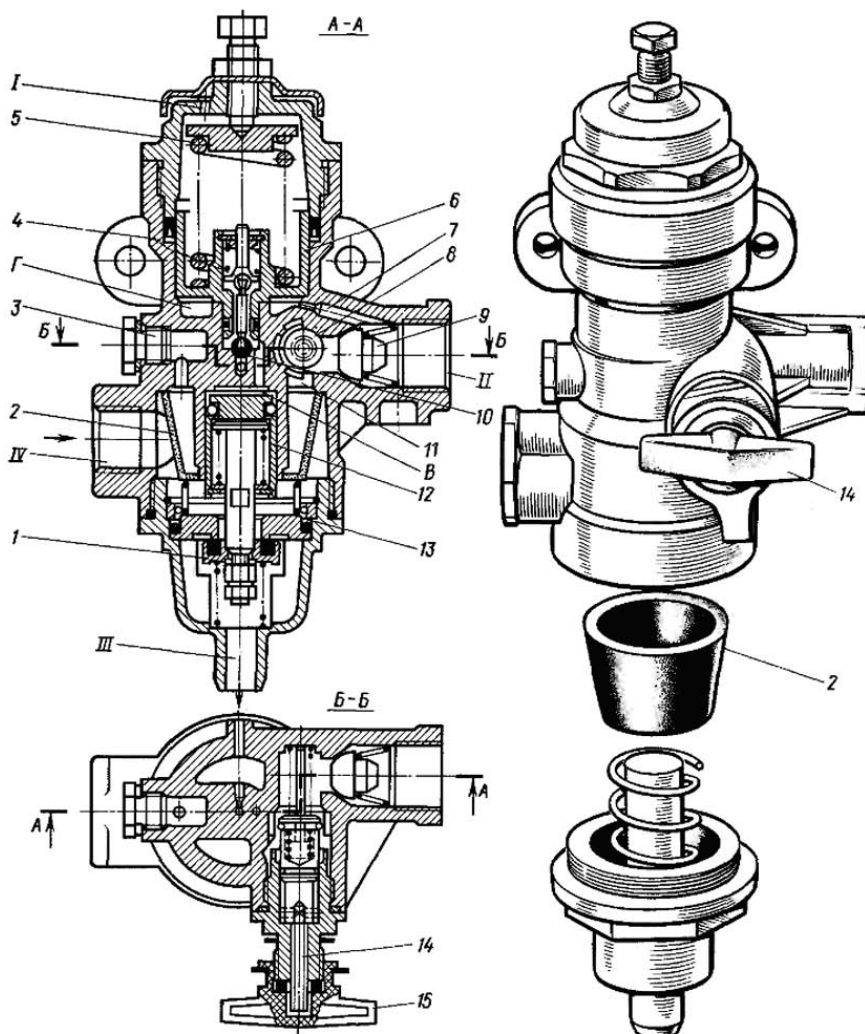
Регулятор давления: В — полость над разгрузочным поршнем; Г — полость под следящим поршнем; I, III — атмосферный вывод; II — вывод в пневматическую систему; IV — ввод от компрессора; 1 — разгрузочный клапан; 2 — фильтр; 3 — пробка канала отбора воздуха; 4 — выпускной клапан; 5 — уравновешивающая пружина; 6 — следящий поршень; 7, 11 — каналы; 8 — кольцевой канал; 9 — обратный клапан; 10 — впускной клапан; 12 — разгрузочный поршень; 13 — седло разгрузочного клапана; 14 — клапан для накачки шин; 15 — колпачок
